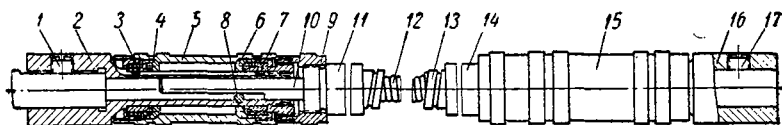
Привод шпинделя 30-шпиндельного сверлильного станка:
